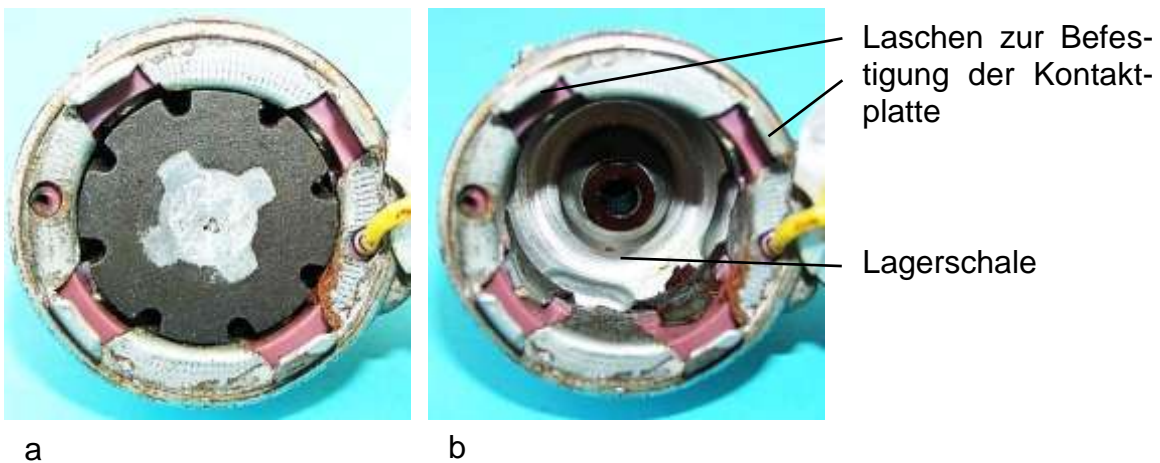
Anker: a) Stirnseiten des Ankers und des Polrades, b) Klauenpolanker im Gehäuse mit den Laschen zur Befestigung der Kontaktplatte
